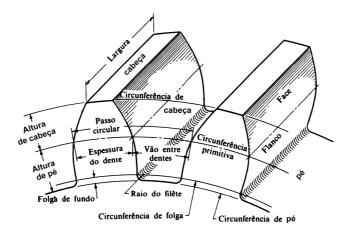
Elementos presentes em uma engrenagem (Buckingham, 1988)
